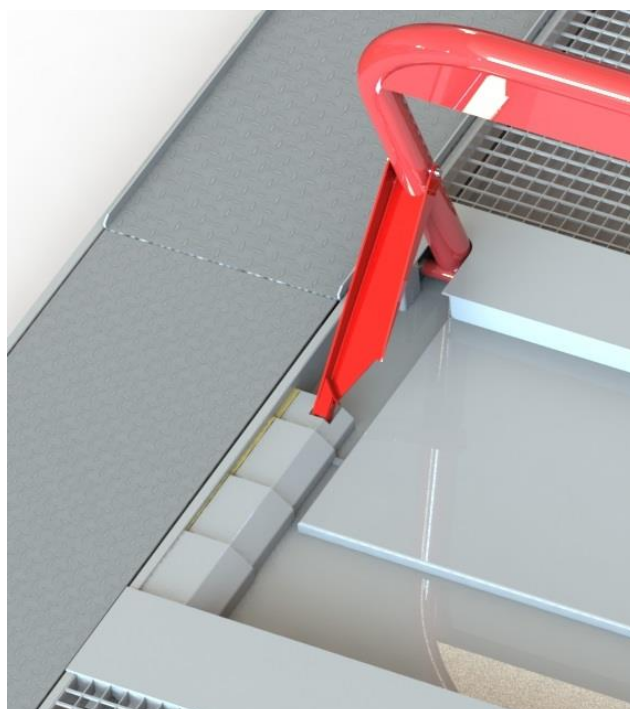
Detail složené zábrany a zasunutých krycích elementů
